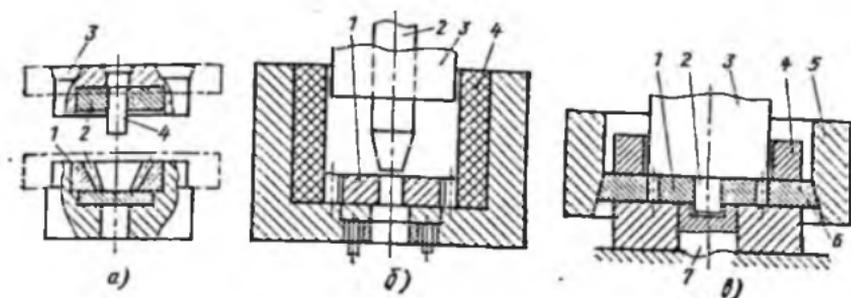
Схемы изготовления шестерен с оформлением зубьев
